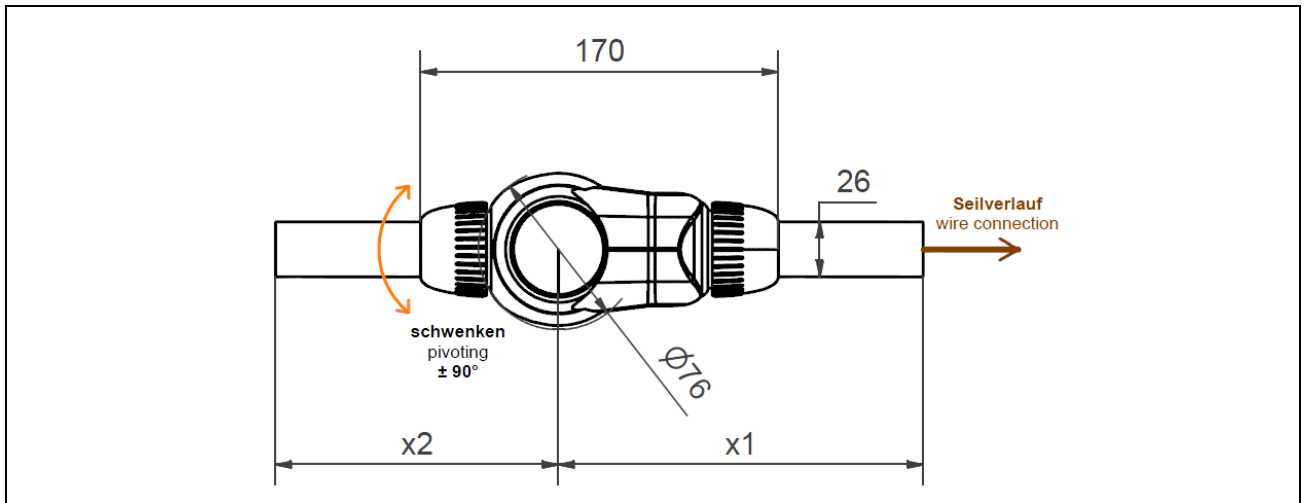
Maßzeichnung Schwenkgelenk RL-50-PL1
